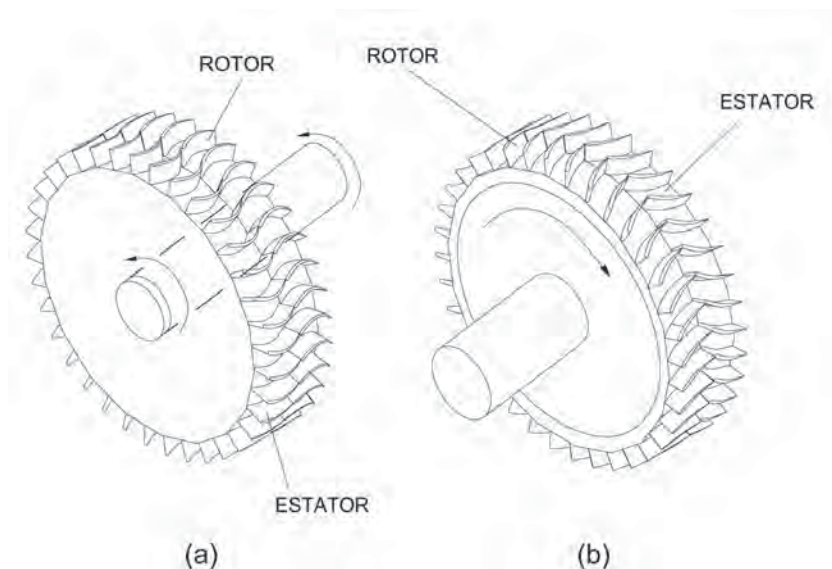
a) turbina elemental axial y b) turbocompresor elemental axial.
